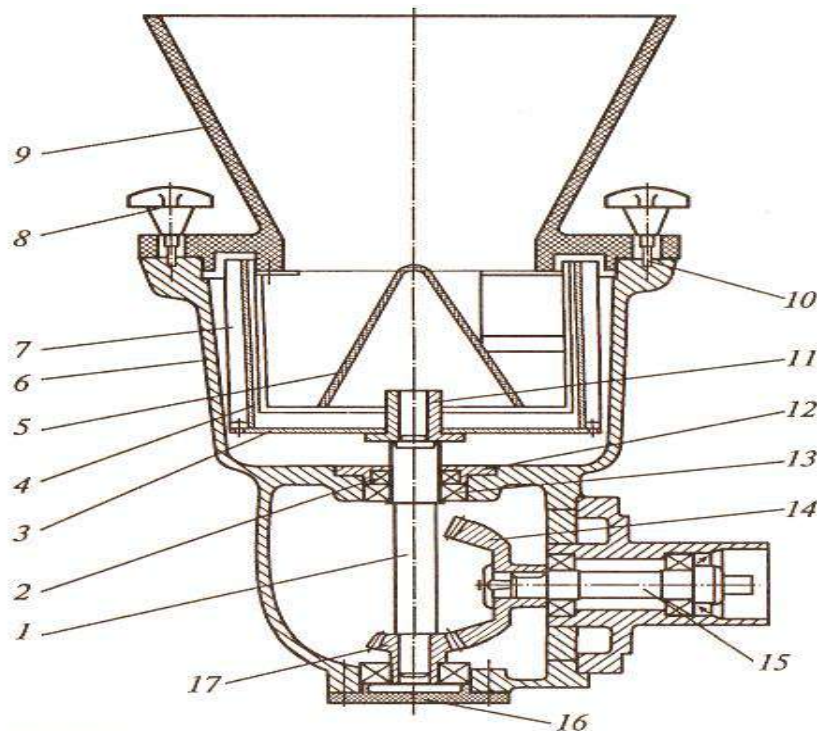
Просіювач МПП-II: 1 – вал; 2 – манжета; 3 – днище; 4 – барабан-сито; 5 – розсікач; 6 – корпус робочої камери і мультиплікатора; 7 – скребок; 8 – гайка; 9 – завантажувальний бункер; 10 – шпилька; 11 – втулка; 12, 16 – кришки; 13 – підшипник; 14, 17 – конічні шестерні; 15 – приводний вал
